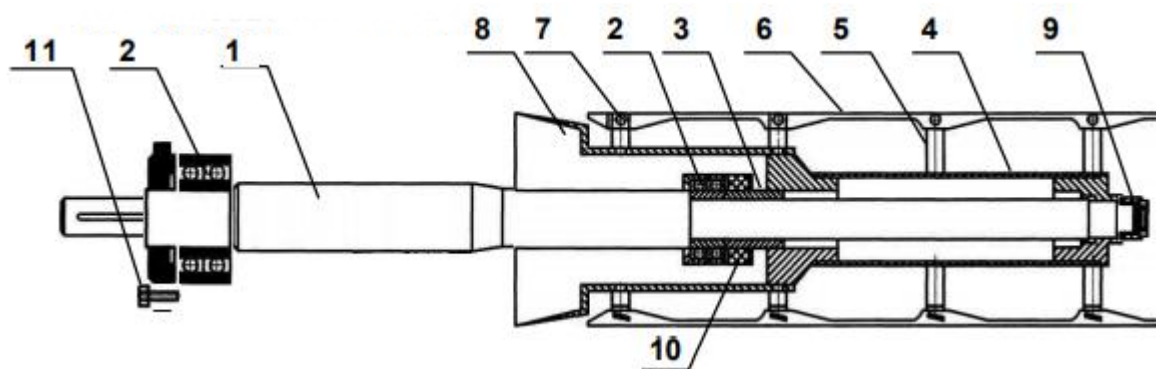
Вал збивача в зборі: 1 - вал; 2 - підшипники; 3 - втулка; 4 - корпус біла; 5 - стійка; 6 - лопата біла; 7 - кріплення лопати; 8 - конус; 9 - гайка спеціальна; 10 - ущільнення; 11 - болтове кріплення
